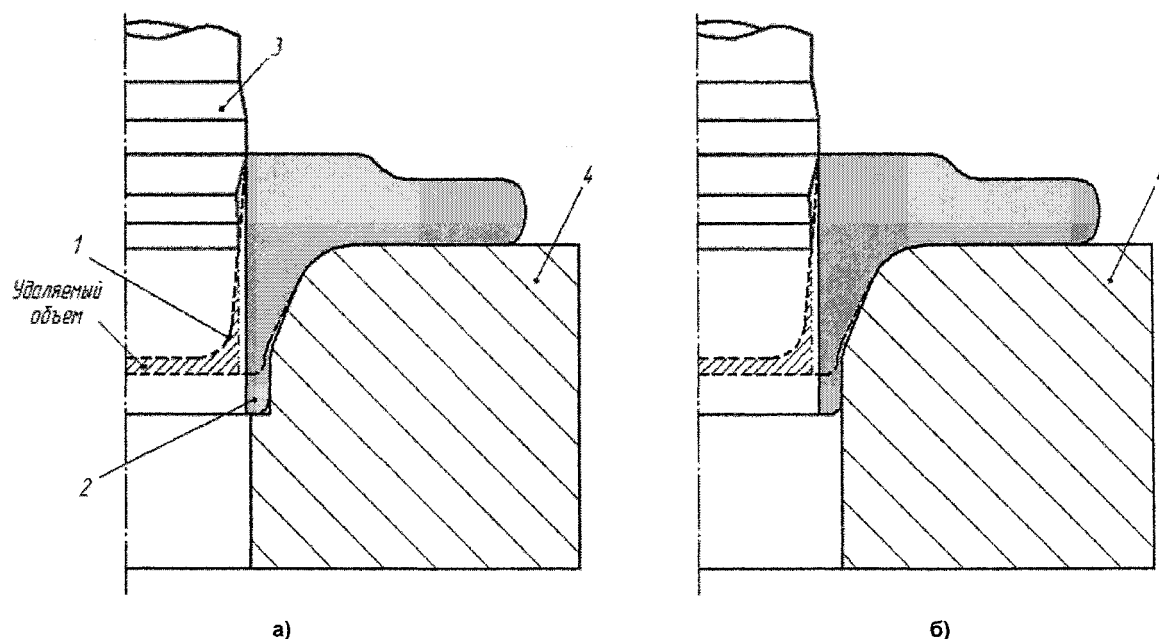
Схема деформации прошивка–раздача–выдавливание/вытяжка–калибровка (ПРВК): а – с закрытой прошивной матрицей; б – с открытой прошивной матрицей; 1 – контур предварительной поковки; 2 – окончательная поковка; 3 – пуансон комбинированный; 4 – матрица прошивная
